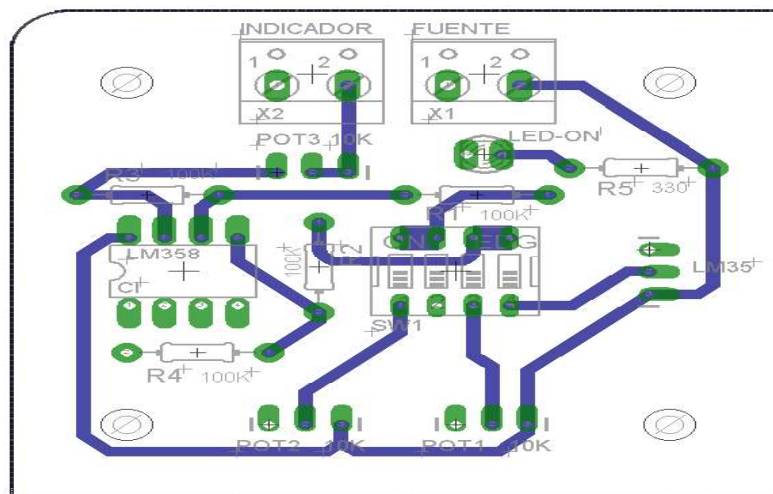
Diseño PCB de la tarjeta KIT INST-01.
